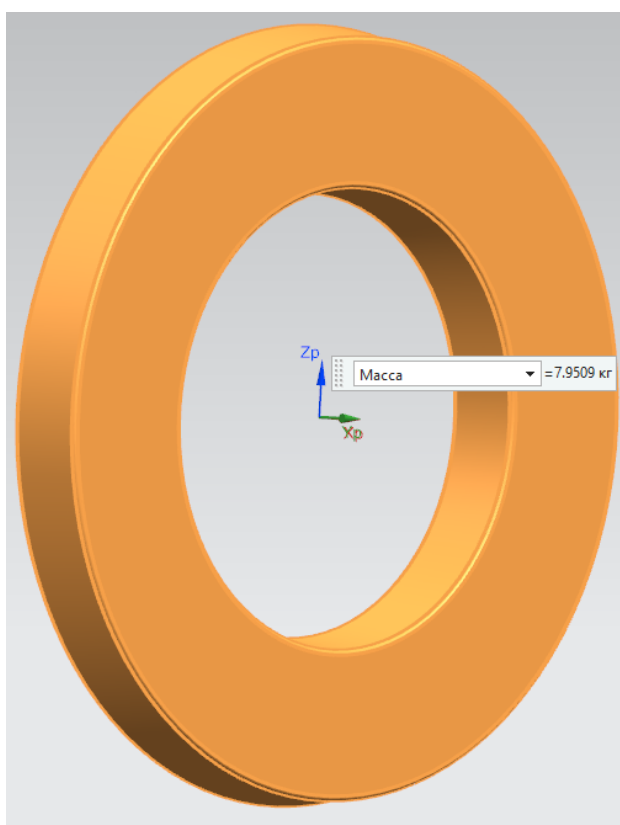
Модель і маса заготовки при виготовленні на ГКМ
